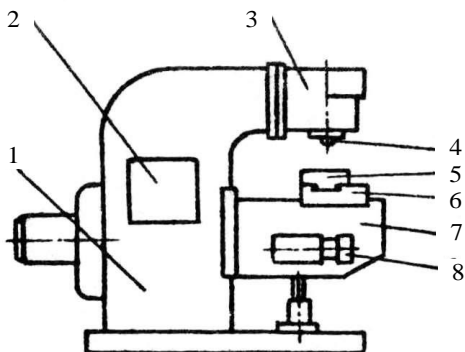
Общий вид вертикально-фрезерного станка:
